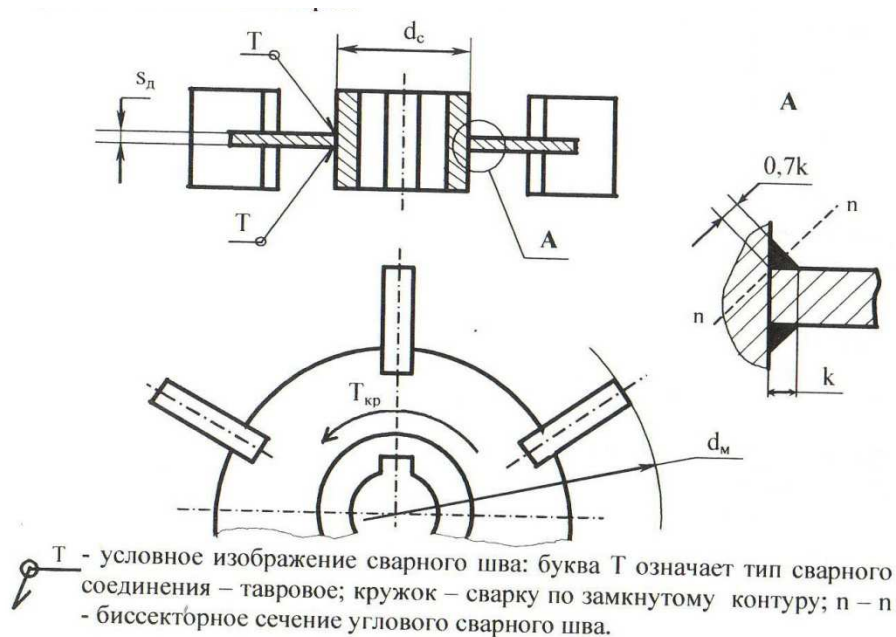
Схема к расчету угловых швов турбинной открытой мешалки
